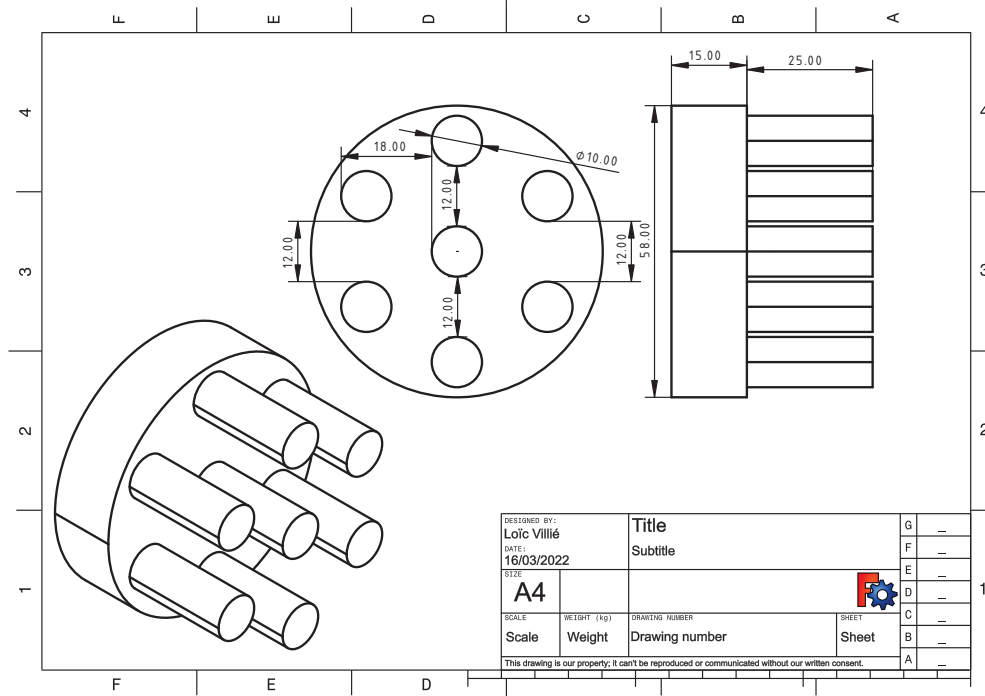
Plan d’usinage des éprouvettes de compression.
